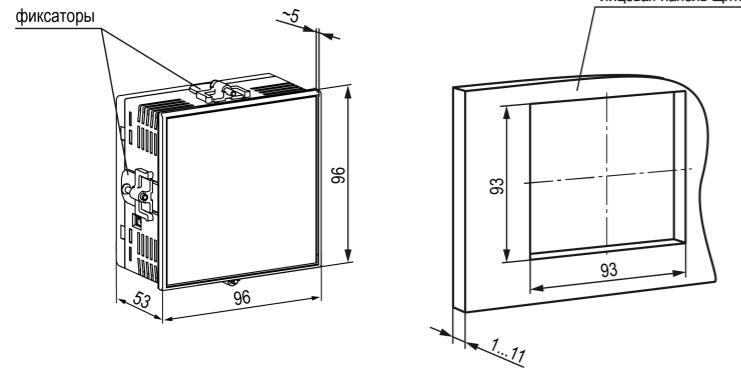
Габаритные размеры корпуса Щ1 и монтажного отверстия в щите
